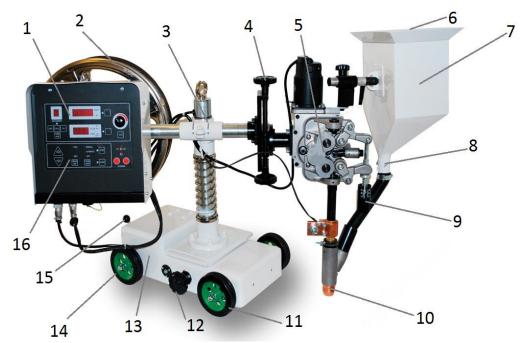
Сварочный трактор Pandaweld 1250:
